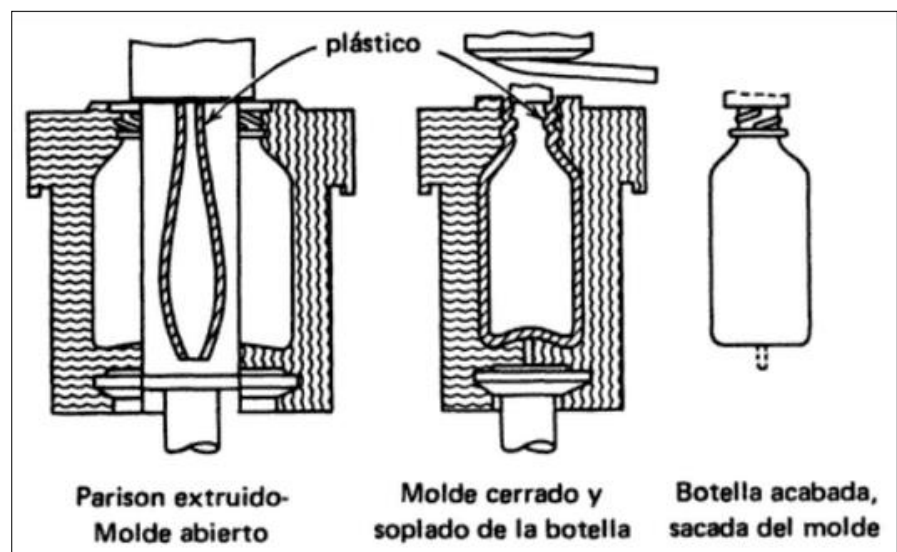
ESQUEMA DE MOLDEO POR SOPLADO [22].
